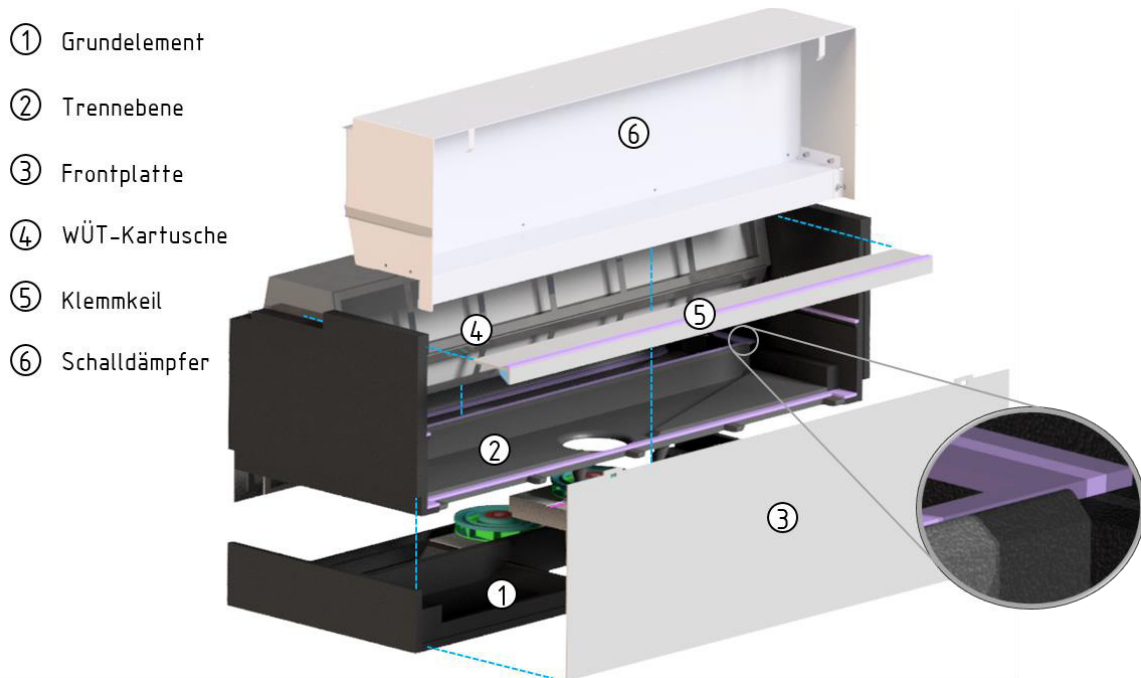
Explosionszeichnung des Prototyp II (ohne Fenster und Außenanbaukomponenten)
